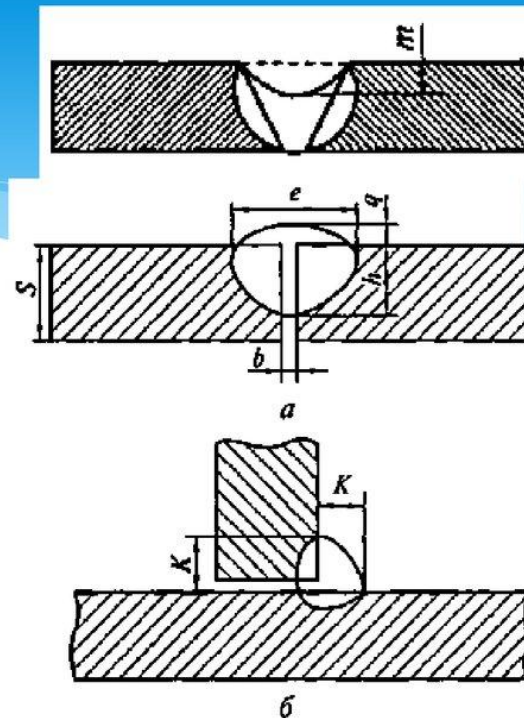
Основные геометрические параметры сварных швов (по ГОСТ 2601—84):
